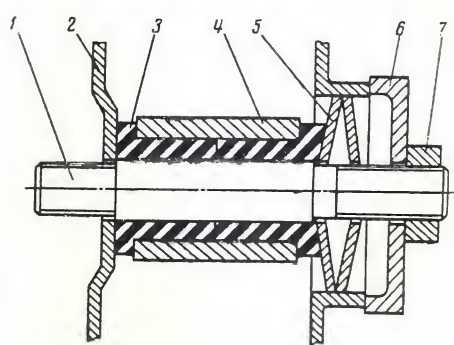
Так работает приспособление: 1 — ось; 2 — кронштейн рессоры; 3 — резиновые втулки; 4 — рессора; 5 — сферическая шайба; 6 — шайба; 7 — гайка.
